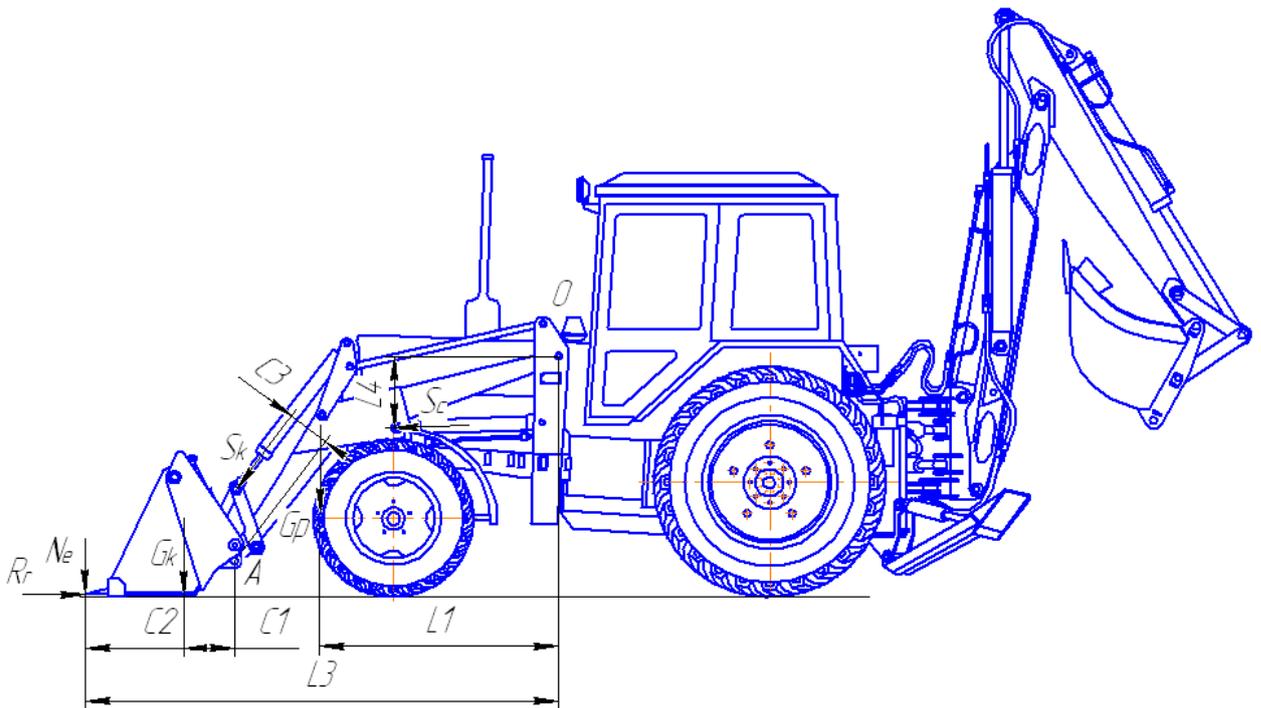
Схема для определения усилий гидроцилиндров погрузочного оборудования
